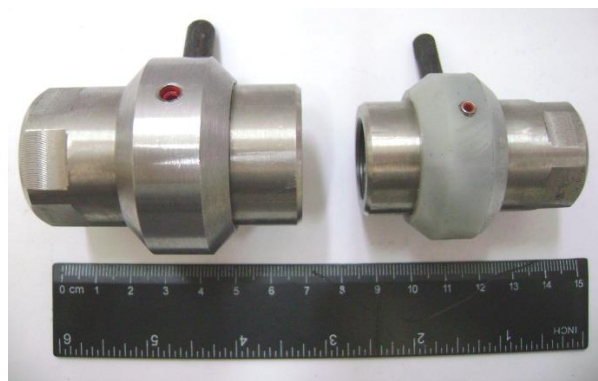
Пруткова заготовка $\varnothing 40$ мм отримана на основі методу ПМ і зварювання після механічної обробки різанням
